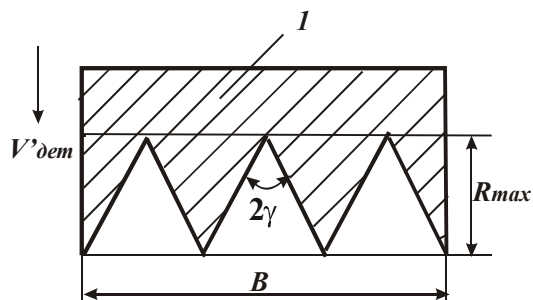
Схема образования шероховатости поверхности: 1 – обрабатываемый материал.
